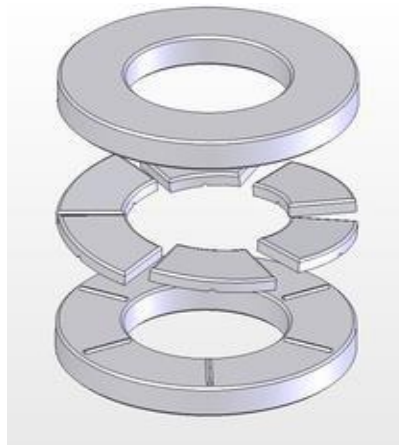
Thrust Bearing. Parte mecánica del motor eléctrico.
